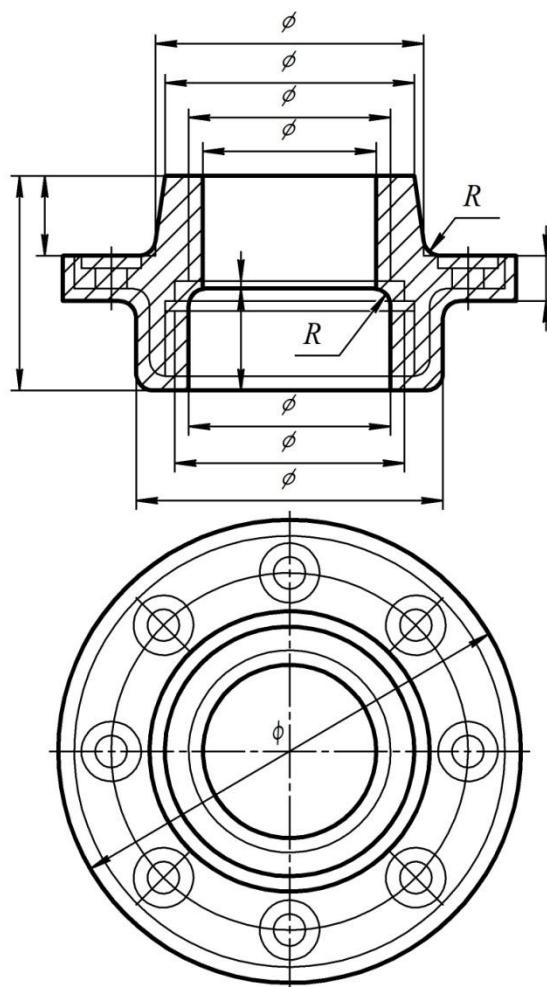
Чертеж отливки, выполняемый на карте операционных эскизов
